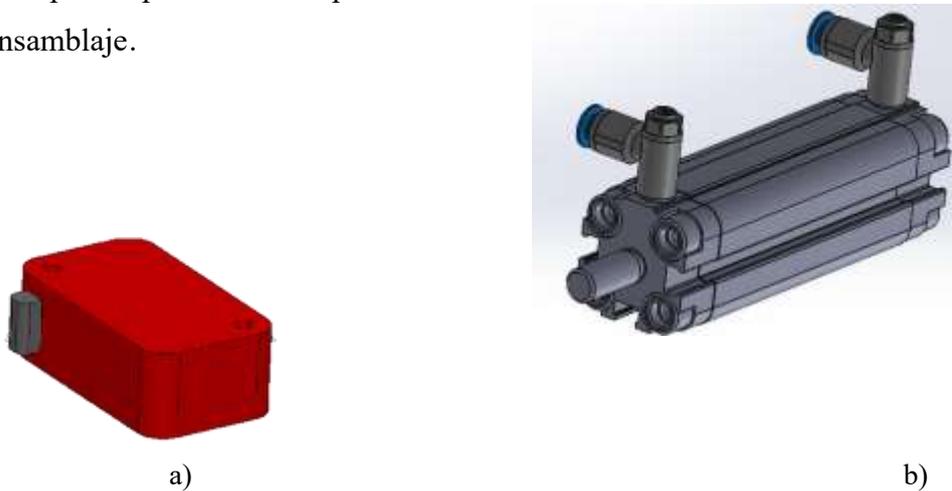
Piezas del primer ensamble a) sensor de detección de la celda b) actuador lineal de doble efecto
